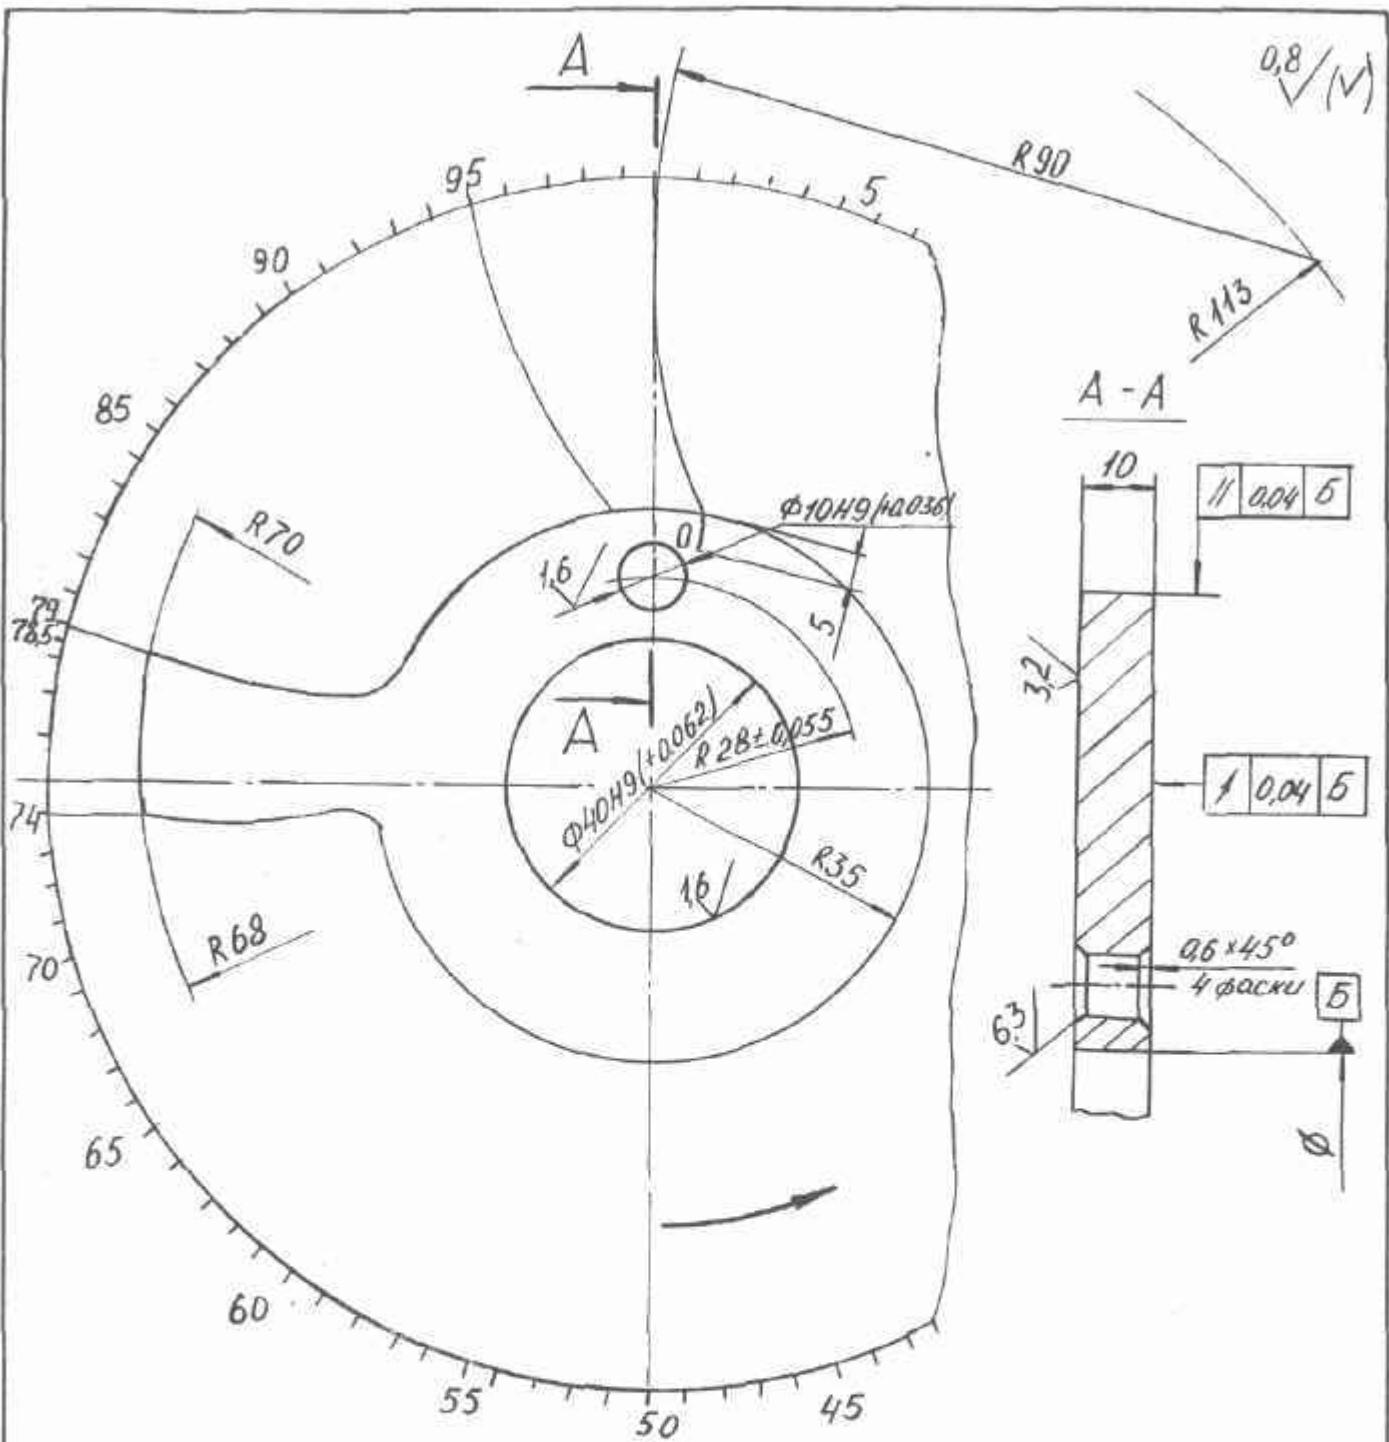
Чертеж заготовки кулачка для многократного отвода револьверного суппорта.
